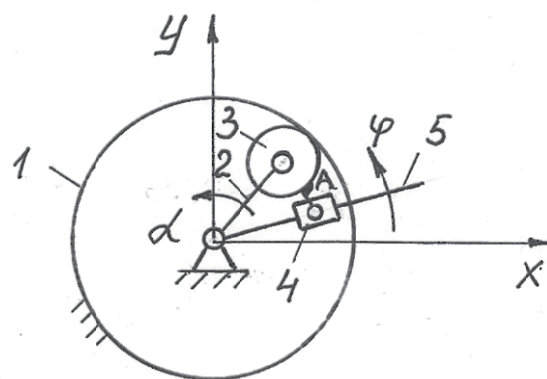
Схема зубчато-рычажного механизма с внутренним зацеплением колес
